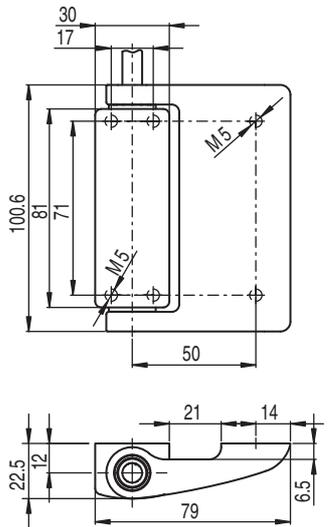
Dimensões do S410-M1CB2-T em mm
